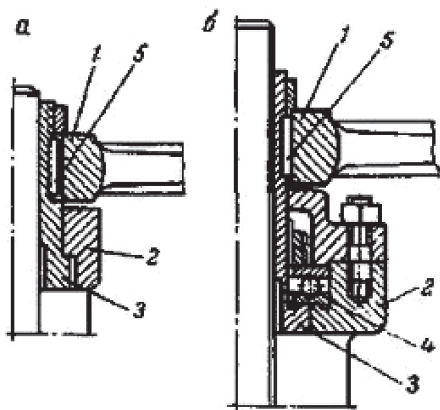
Конструкции опоры втулки маховика: а — скольжения; б — качения; 1 — маховик; 2 — крышка задвижки; 3 — ходовая гайка; 4 — подшипник качения; 5 — шпонка
